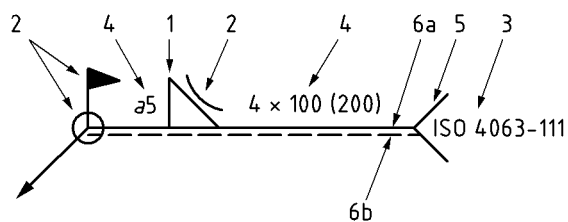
根据焊缝质量等级标注的焊接符号示例
